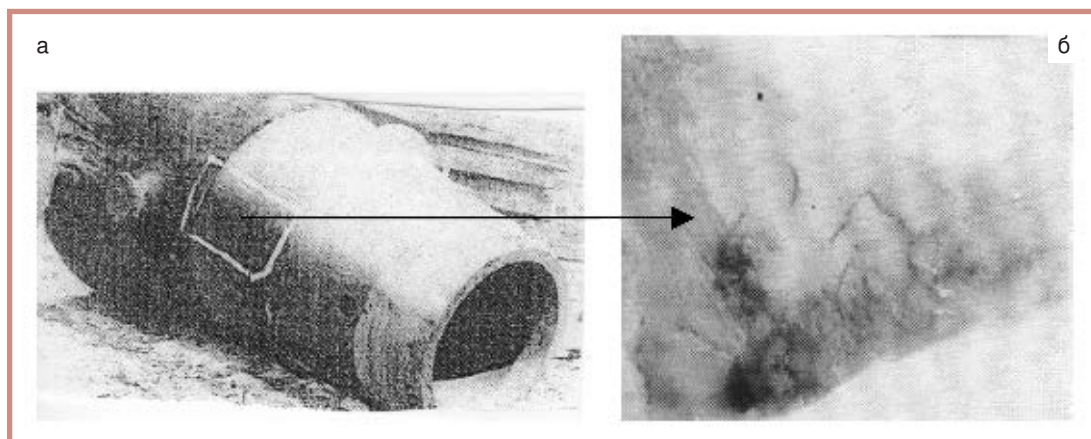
Типичная массивная отливка сложной формы — корпус конуса дробилки (толщина 160–500 мм, масса 30 т, сталь 35Л) (а) и трещины группового характера (б) в местах локального расположения серы (4-й балл по шкале Баумана), образовавшиеся в местах размерной лезвийной обработки
